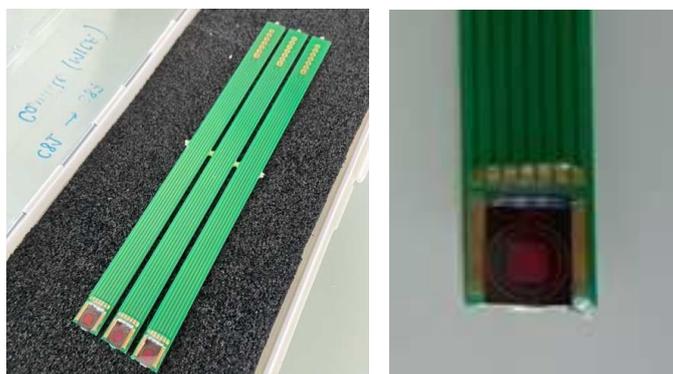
Photographies des capteurs montés sur PCB bâtonnets en vue des pré-tests
